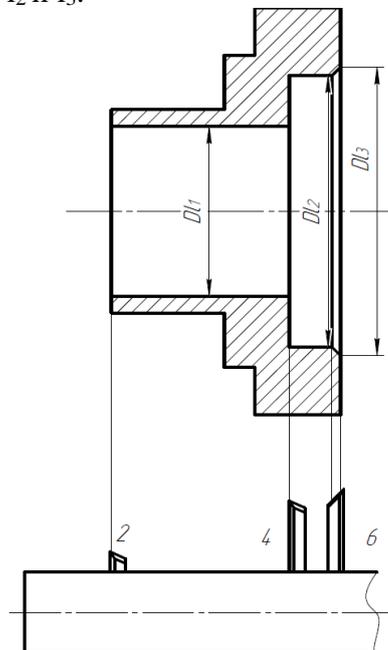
Типовая деталь «Втулка» и схема расположения резцов
